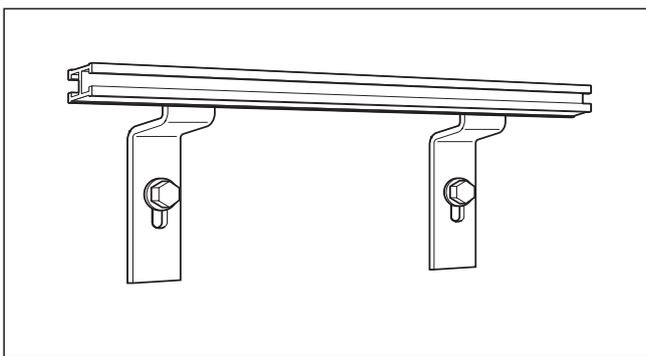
Верхняя пара крюков при монтаже на фасаде
